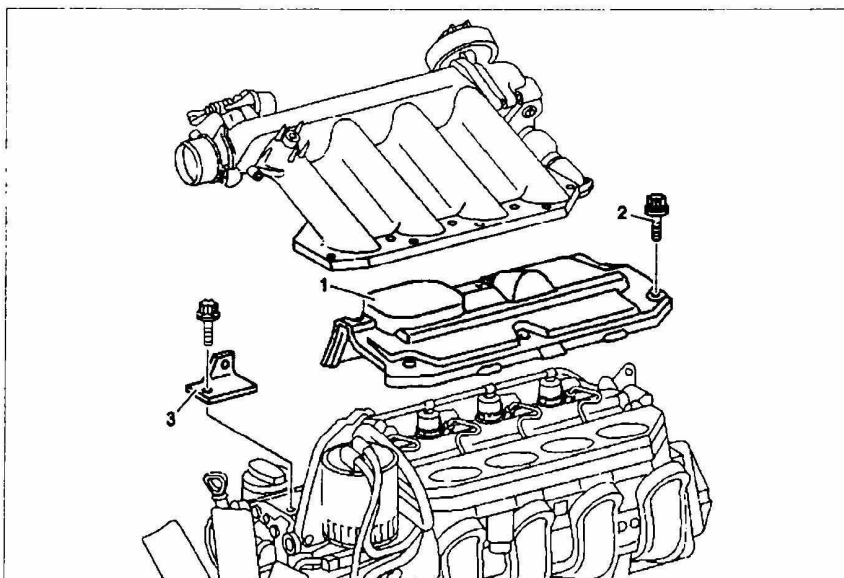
Снятие и установка декоративной панели крышки головки блока цилиндров (показано на двигателях 611):
